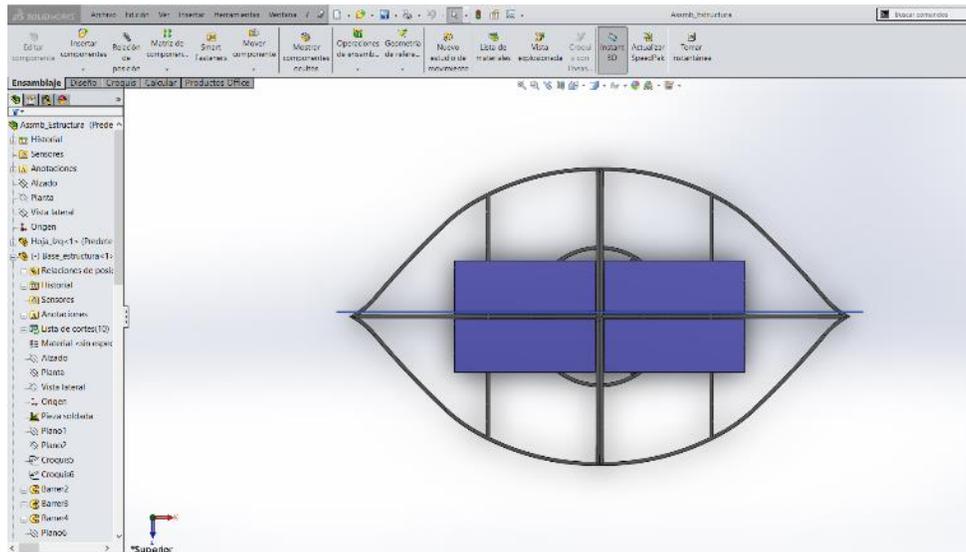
vista superior estación solar. Fuente: Archivo del autor.
